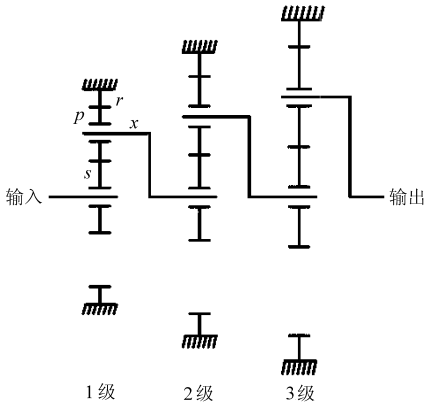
2K-H(NGW)型 3 级行星齿轮减速器机构传动简图
